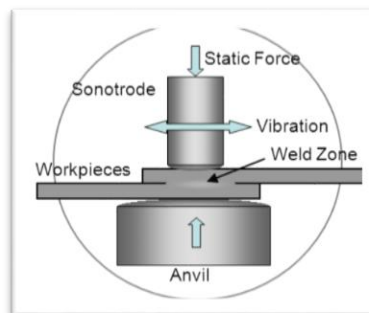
(Esquema de la soldadura por ultrasonidos)
